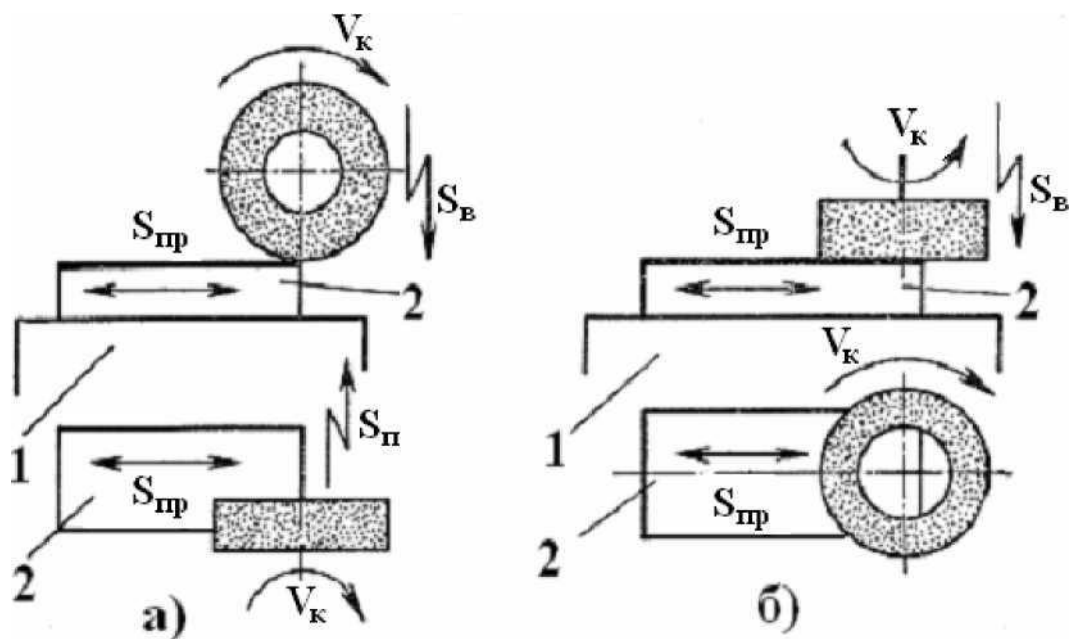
Обработка заготовок на плоскошлифовальных станках: а - шлифование периферией круга; б - шлифование торцом круга
